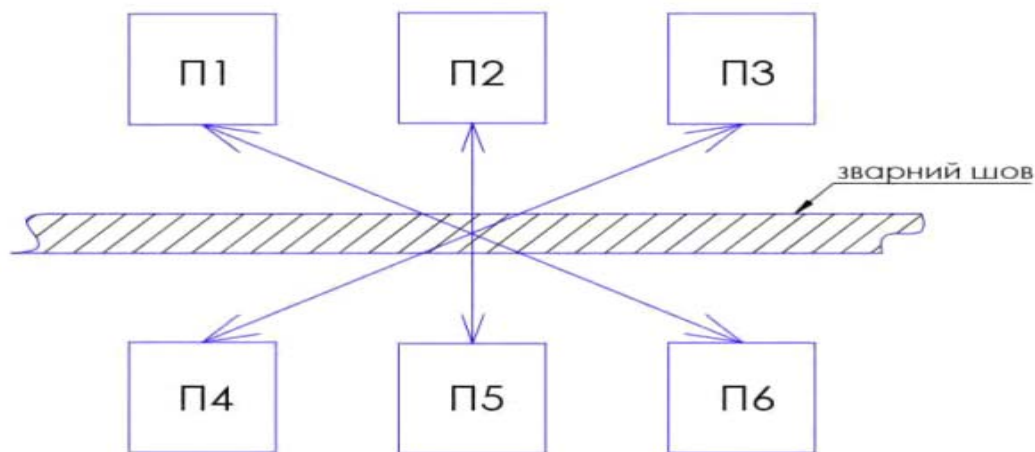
Ж-образна схема контролю зварних з'єднань труб
